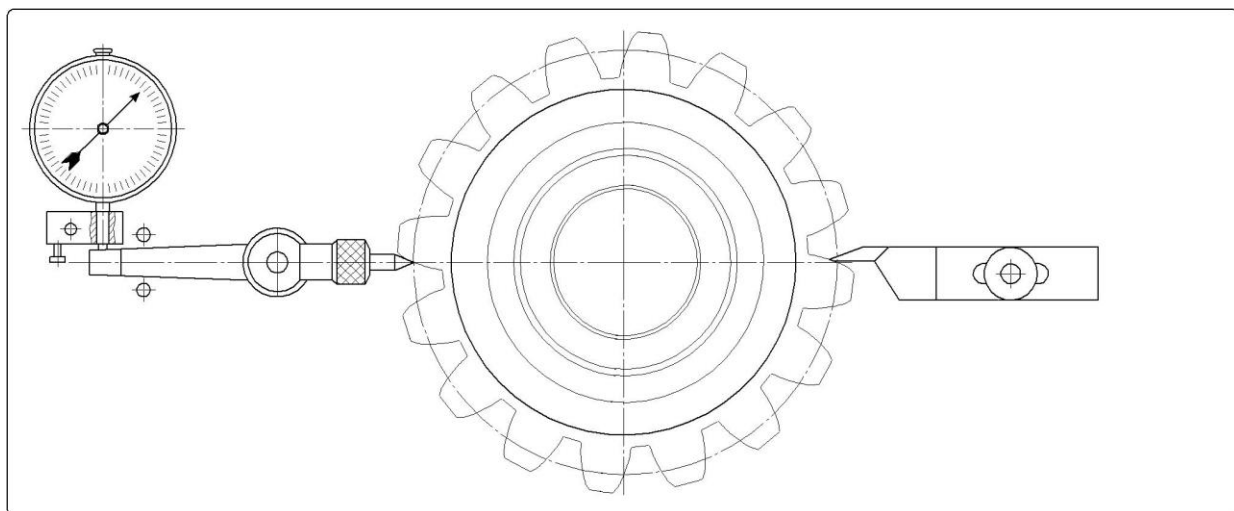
Приспособление для контроля наибольшей погрешности окружного шага долбяка
